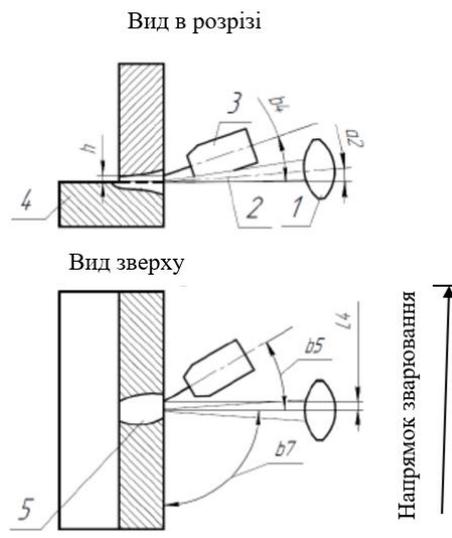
Схема ГЛДЗ, метод «Гібрид» кутового зварного з'єднання в горизонтальному положенні (РА):
